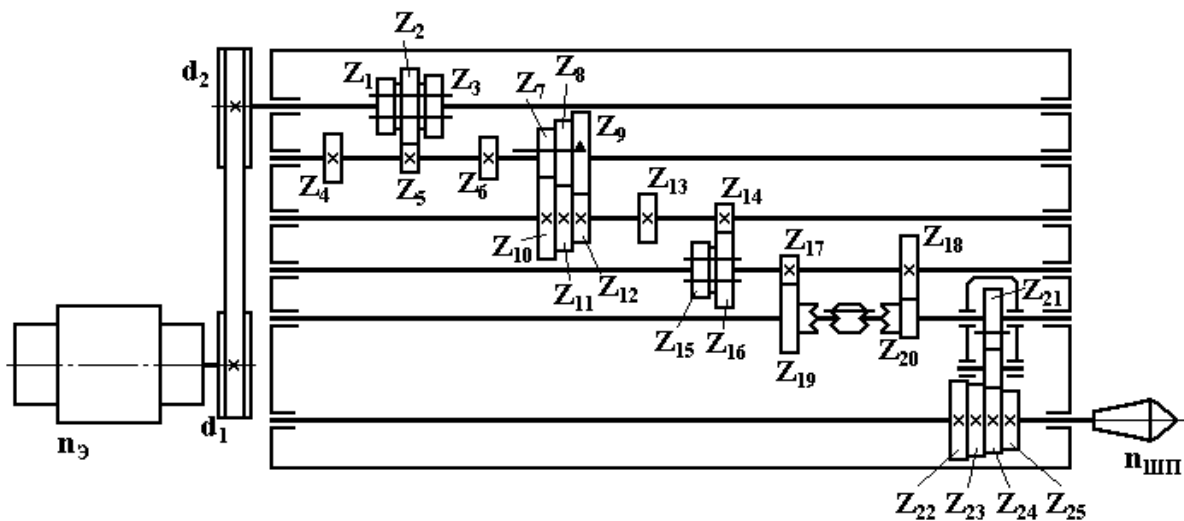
Кинематическая цепь главного движения условного станка (вариант № 2)
